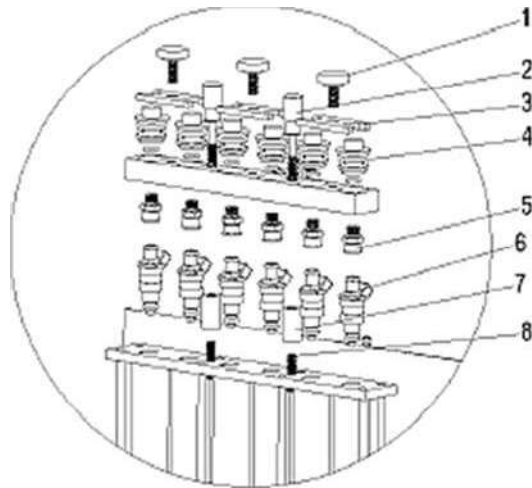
Схема установки паливної рампи для форсунок з верхньою подачею палива:
